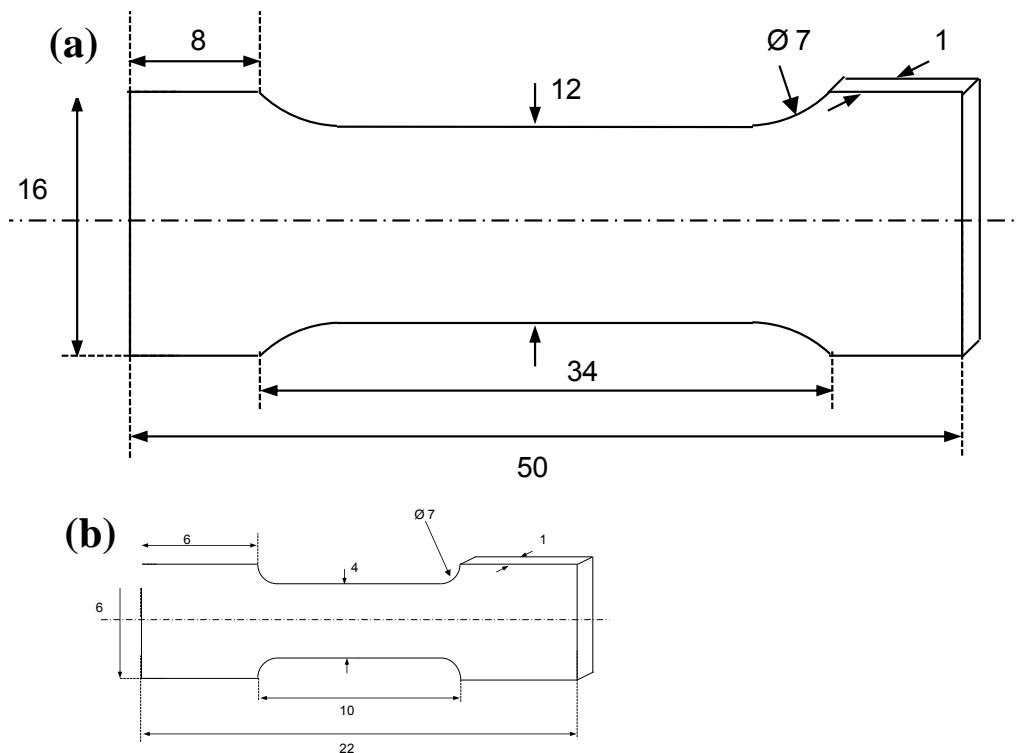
Dimensions des éprouvettes : (a) grande éprouvette (GE), (b) petite éprouvette (PE).
